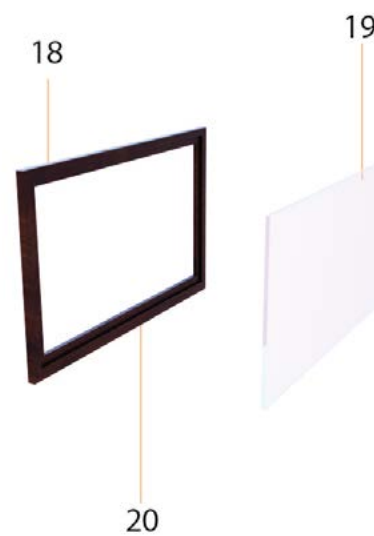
Detalle constructivo 3d puerta con madera MDF
